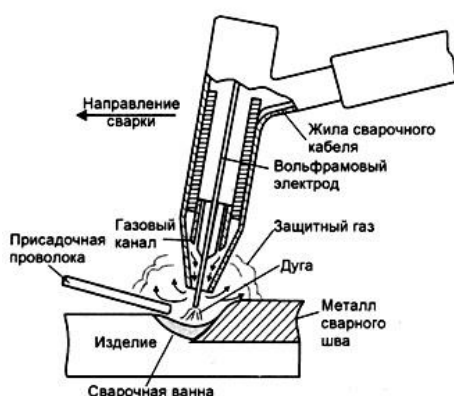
Схема ручной аргонодуговой сварки
